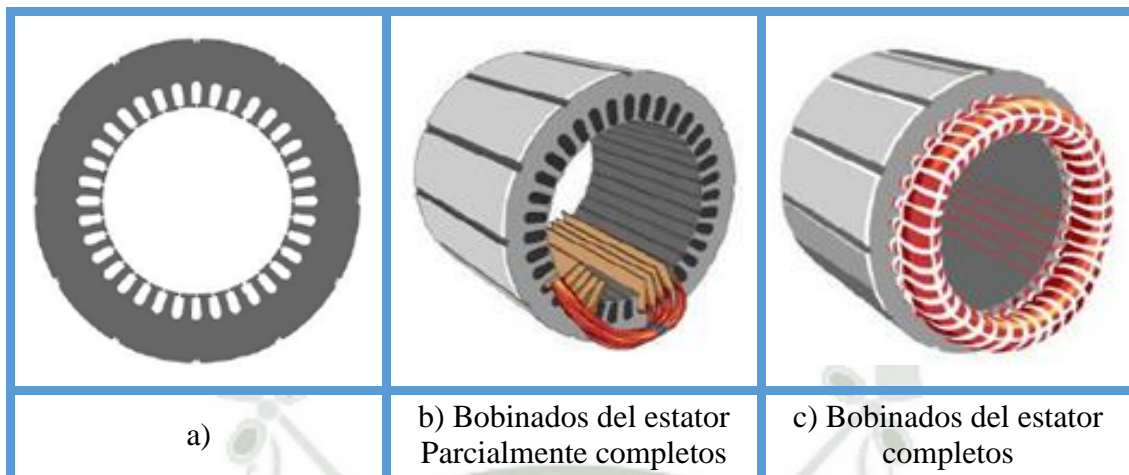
Disposición geométrica y montaje del estator en un motor AC trifásico de inducción.
